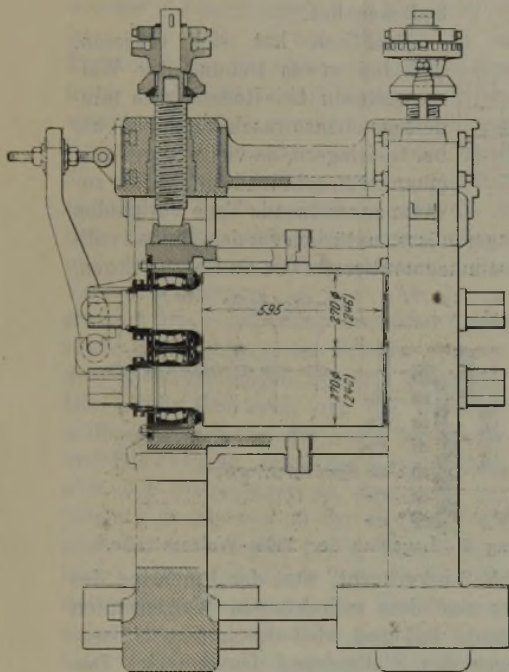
270er-Walzgerüst mit Rollenlagereinbau.
